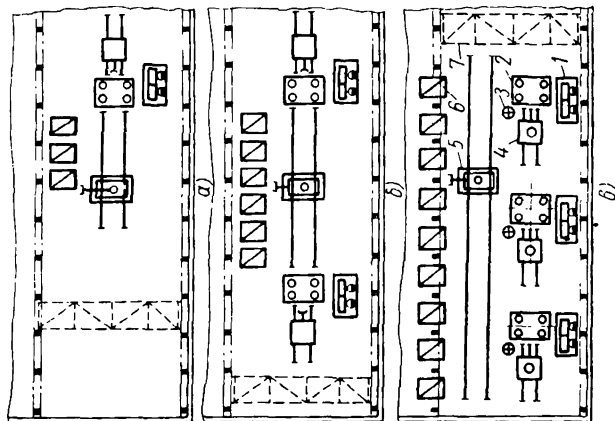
Расположение рельсовой посадочной машины в агрегатах у ковочных прессов: а — при одном ковочном прессе; б — при двух ковочных прессах; 1 — пульта управления; 2 — ковочный пресс; 3 — поворотный стол; 4 — ковочная машина; 5 — рельсовая посадочная машина; 6 — нагревательная печь; 7 — мостовой кран
